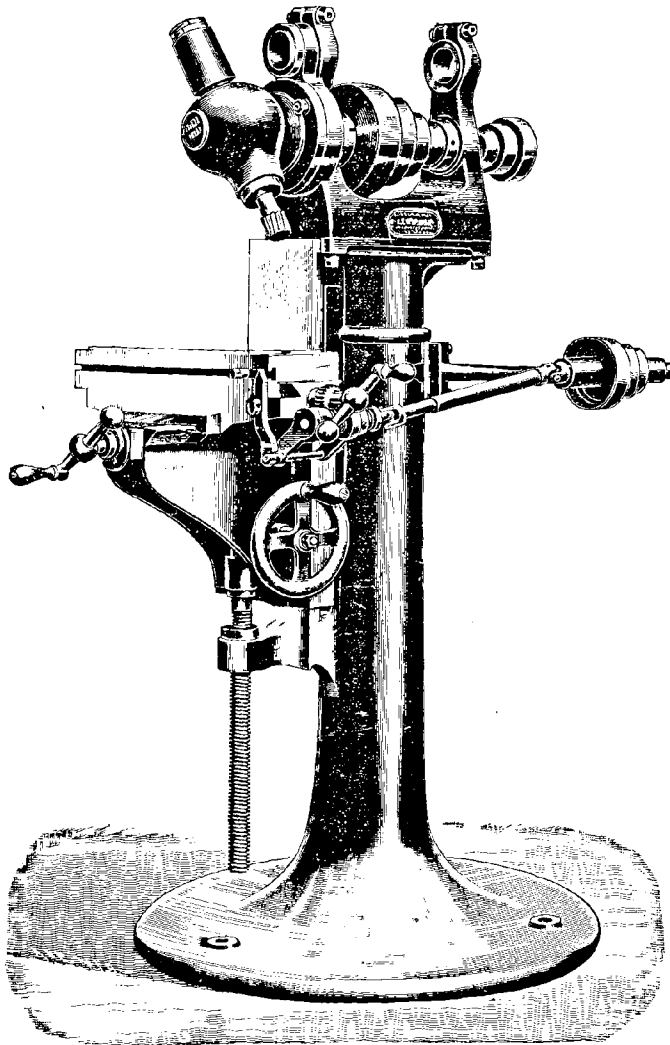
Petite machine à fraiser du « Progrès Industriel ».
